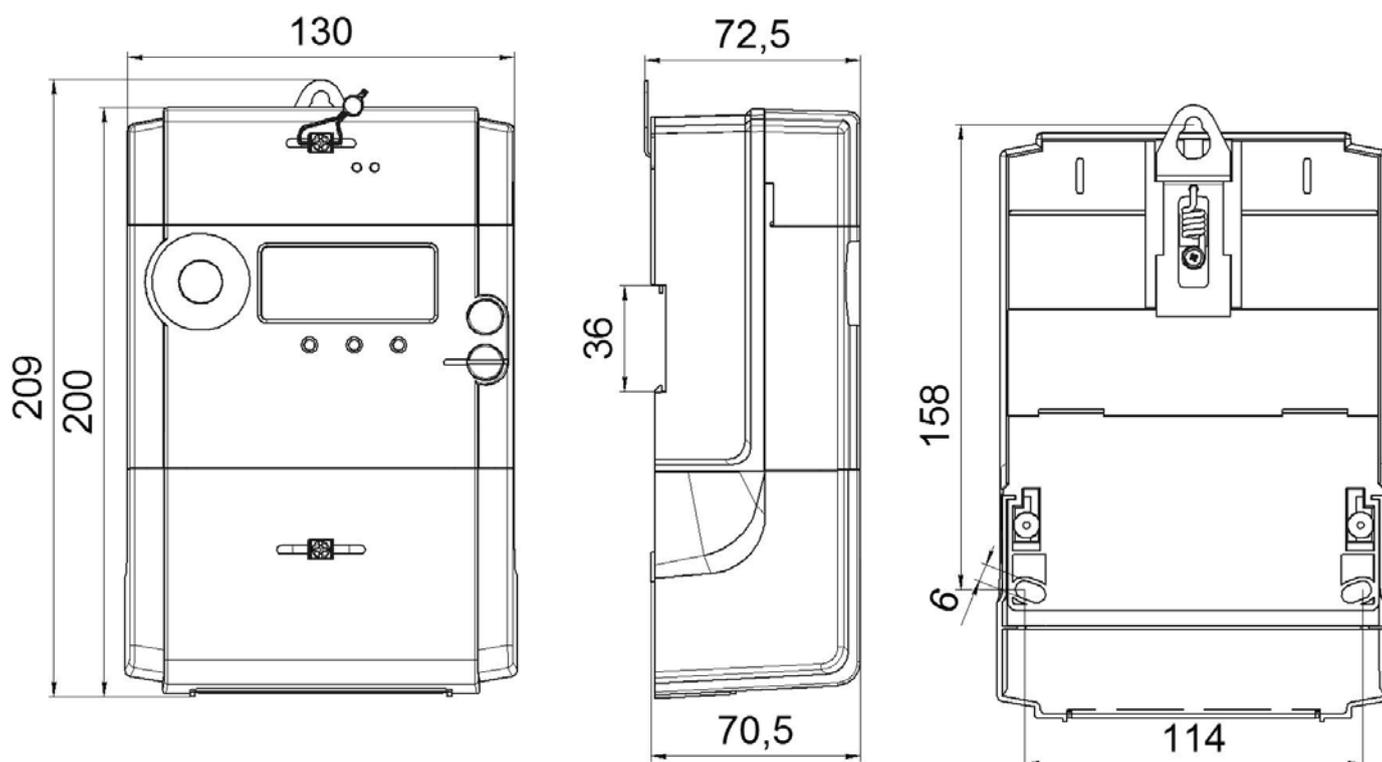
Установочно и габаритные размеры прибора учёта типа TE71 MP-1-3N.
